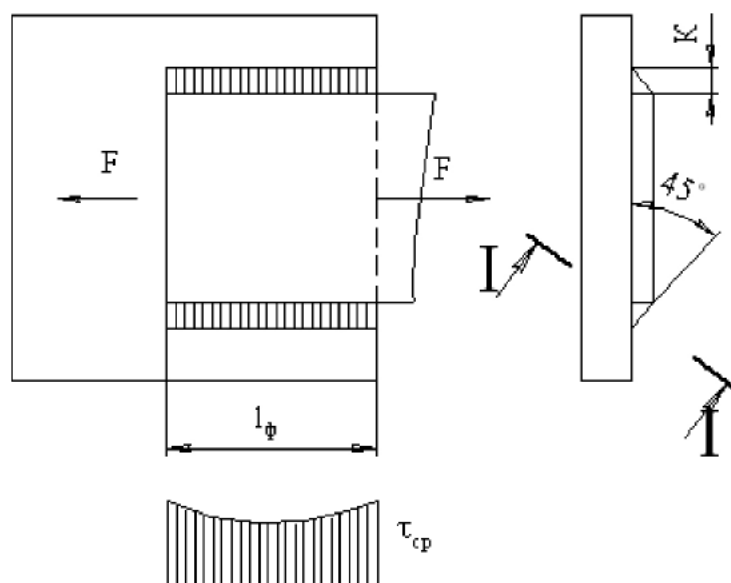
Напряжения во фланговом сварном шве
